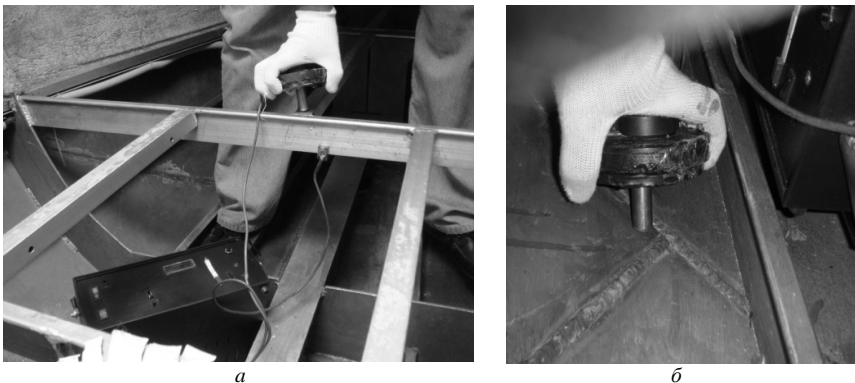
Электродинамическая обработка сварных ремонтных швов корпуса судового корпуса
